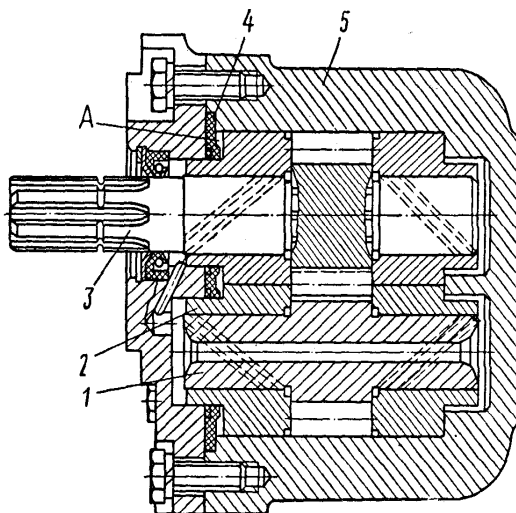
Шестеренный насос типа НШ 46: 1,3- ведомая и ведущая шестерни; 2- втулки; 4- уплотнение; 5- корпус.
